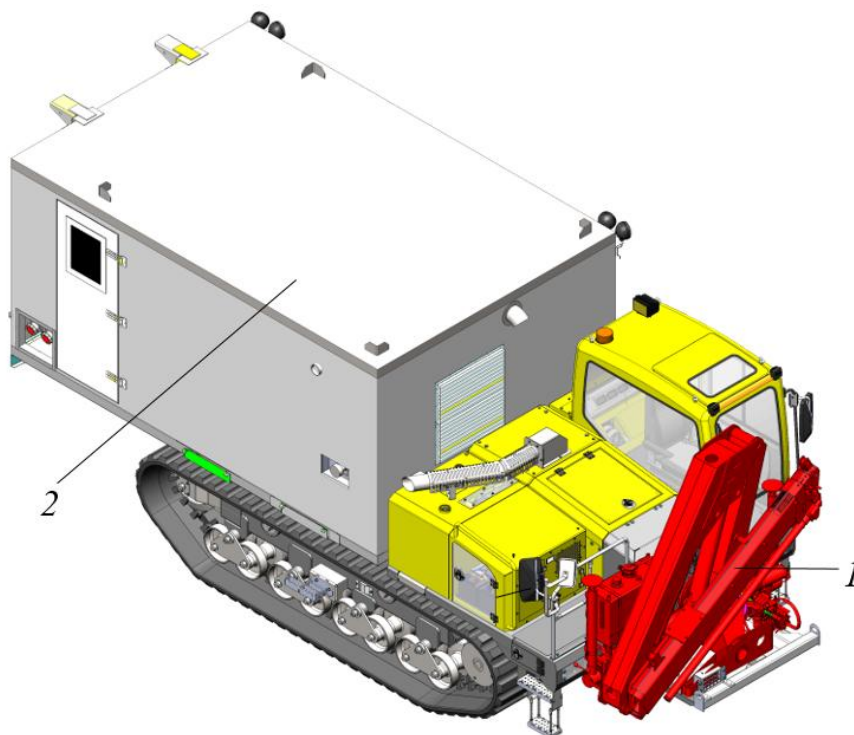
Агрегат гусеничный сварочный
